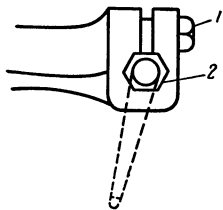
Положение крепящей гайки при установке нитепритягивателя
